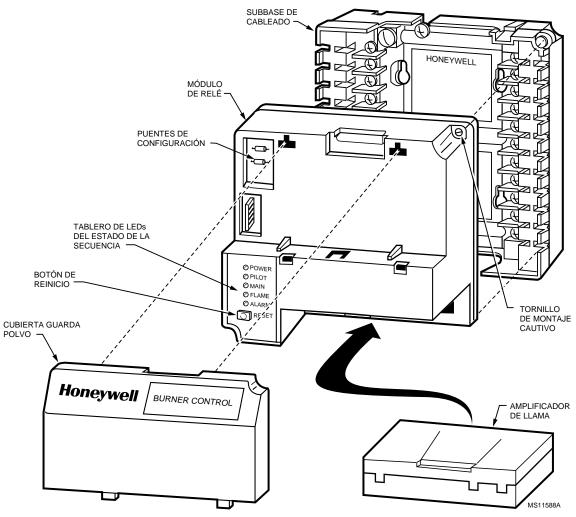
Vista de despiece del Módulo De relé EC/RM7890.
